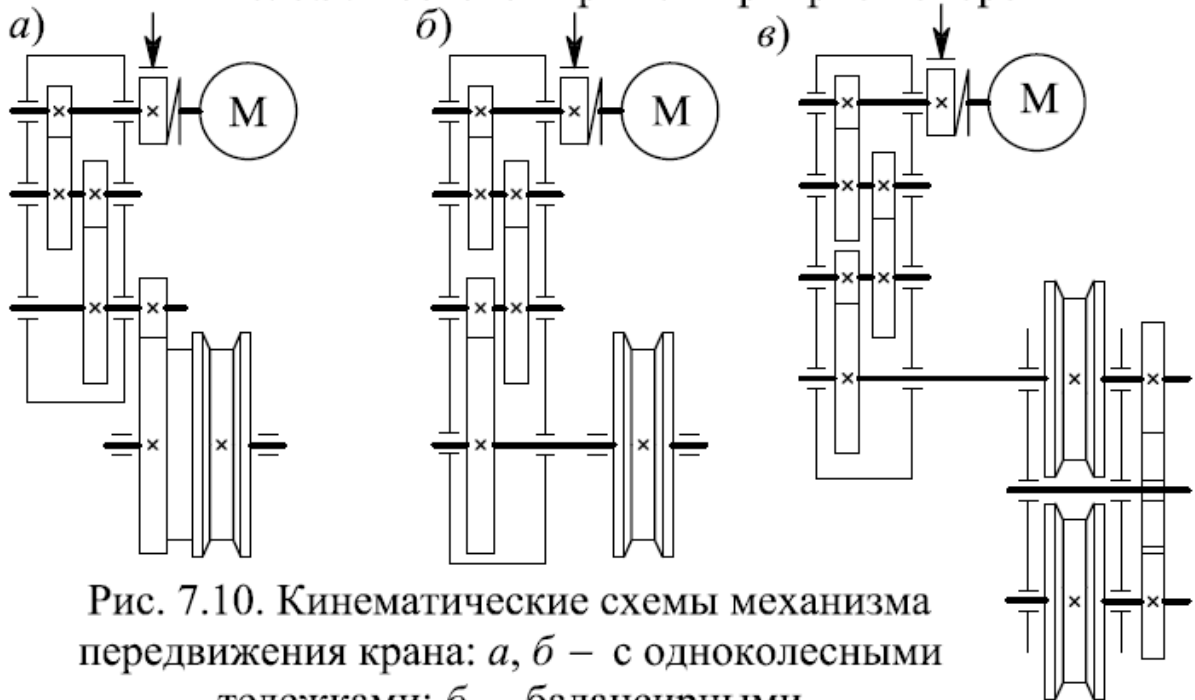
Кинематические схемы механизма передвижения крана: *а, б* – с одноколесными тележками; *в* – балансирными
